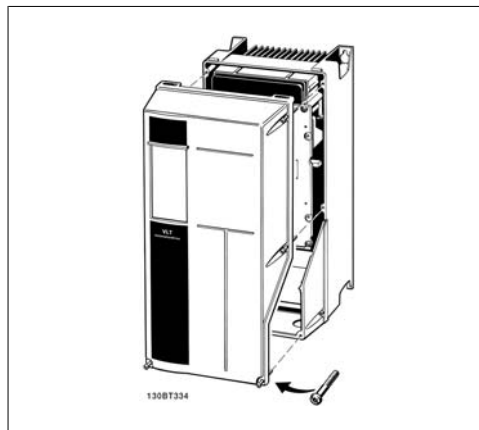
Корпуса A5, B1, B2 C1 и C2
